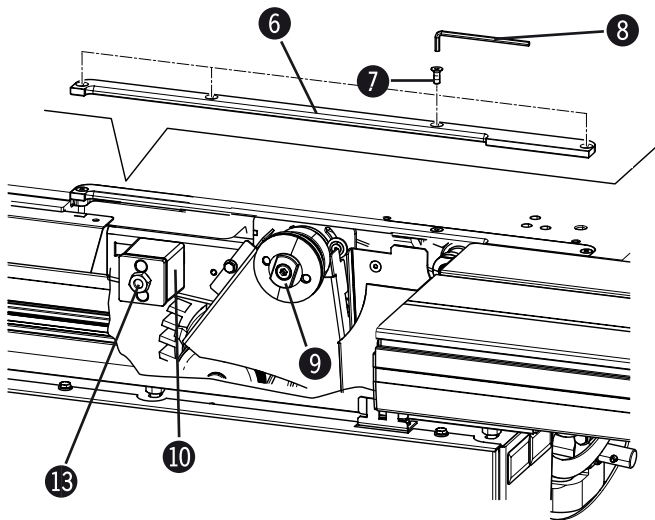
Hinterer Flansch/Spaltkeilhalter/Einlegebrett
